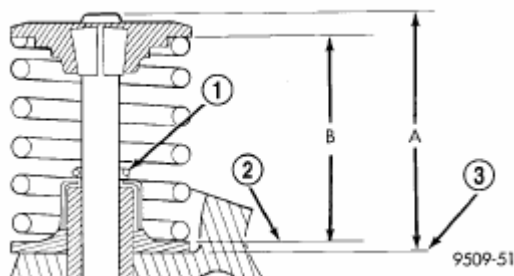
Проверка высоты установки пружины В и размера выступания стержня клапана над опорной поверхностью головки блока цилиндров А.
